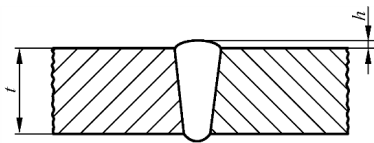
焊缝余高示意图(适用于焊接侧余高)
